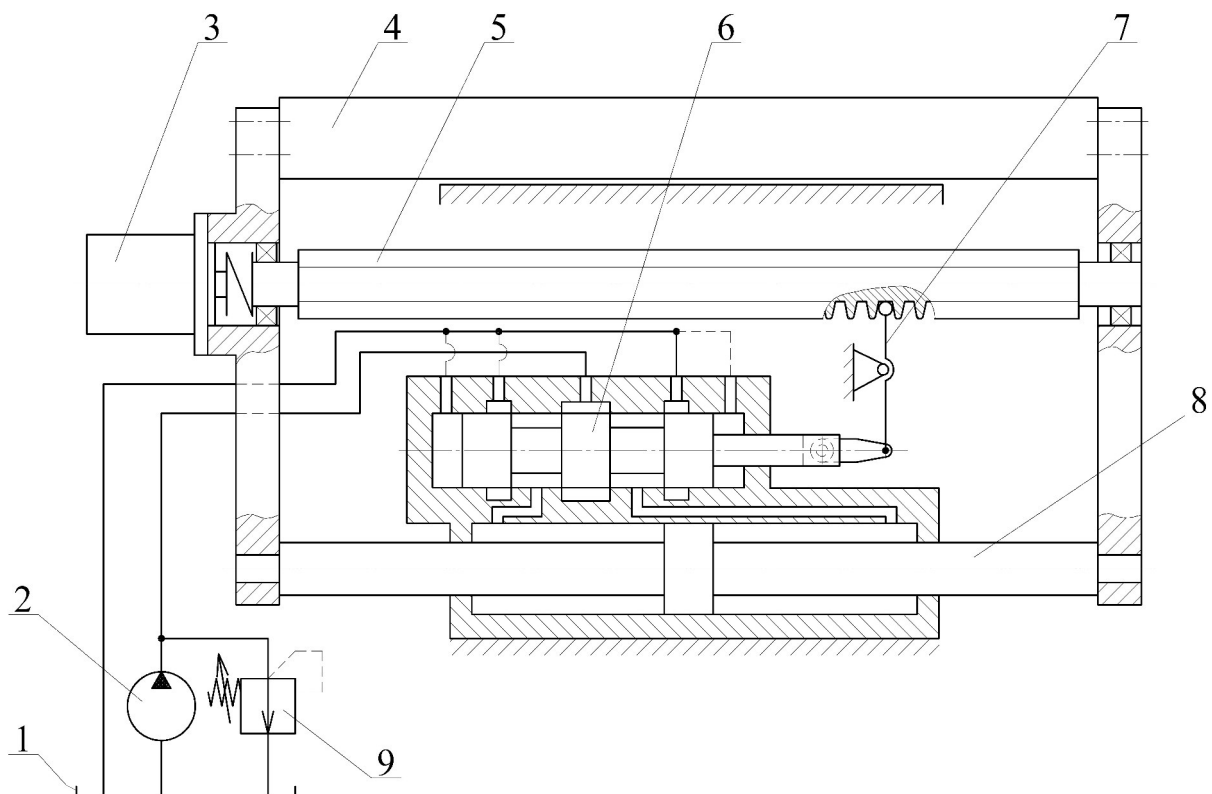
Схема електрогідравлічного слідкувального крокового приводу подачі фрезерного верстата з ЧПК моделі ЛТ-260Ф3
